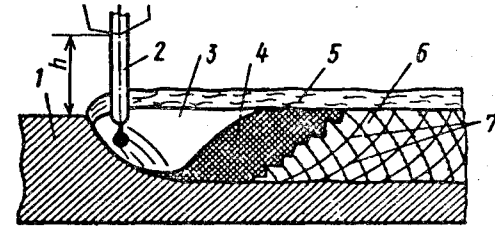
Плавильное пространство при сварке под флюсом: 1 — основной металл; 2 — электродная проволока; 3 — передняя часть сварочной ванны; 4 — хвостовая часть сварочной ванны (жидкий металл); 5 — флюс; 6 — закристаллизовавшийся сварной шов; 7 — границы кристаллизационных слоев, h — вылет электрода
